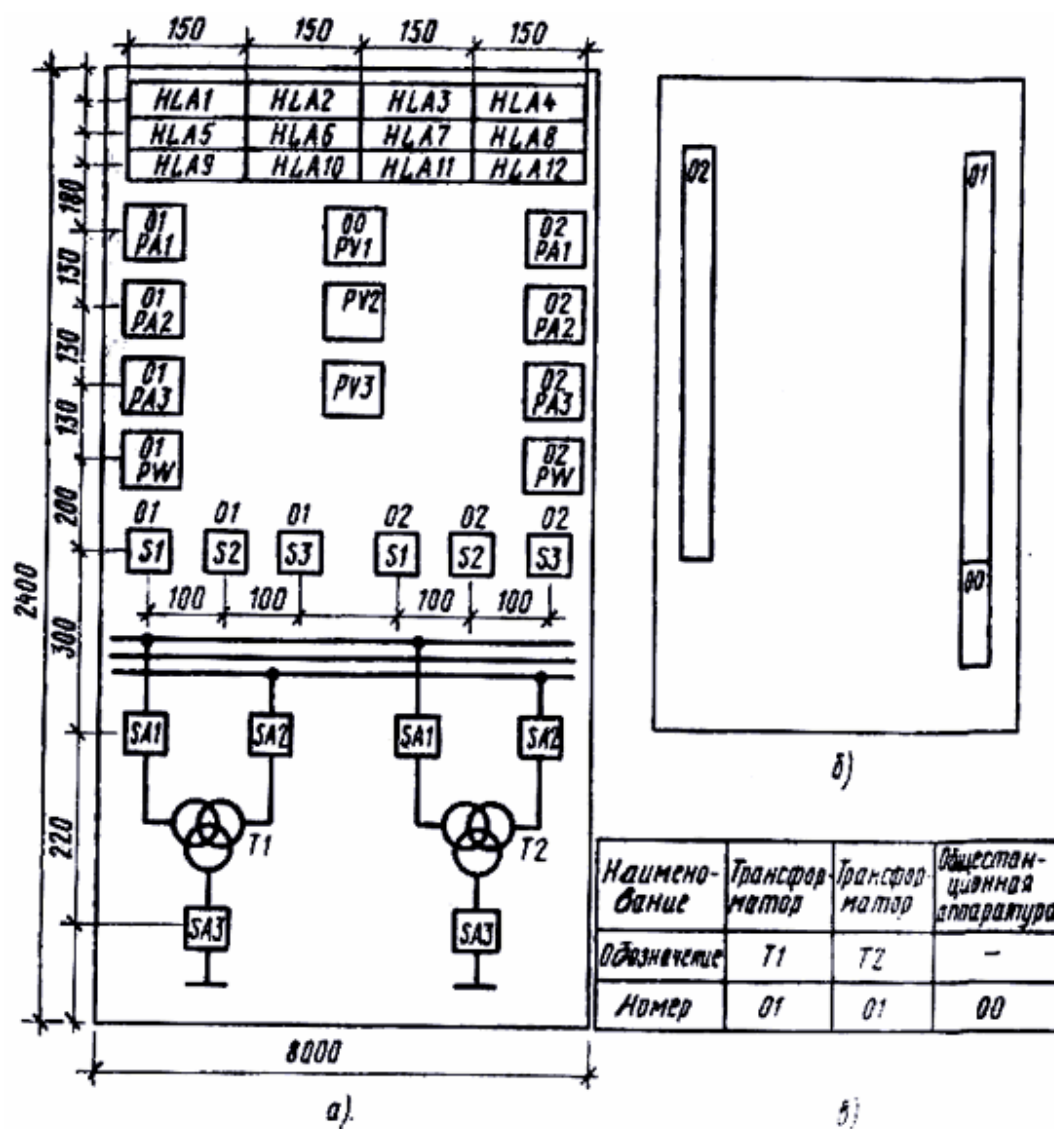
Вид панели с фасадной (а) и монтажной (б) сторон и перечень монтажных единиц (в) на чертеже общего вида панели управления
